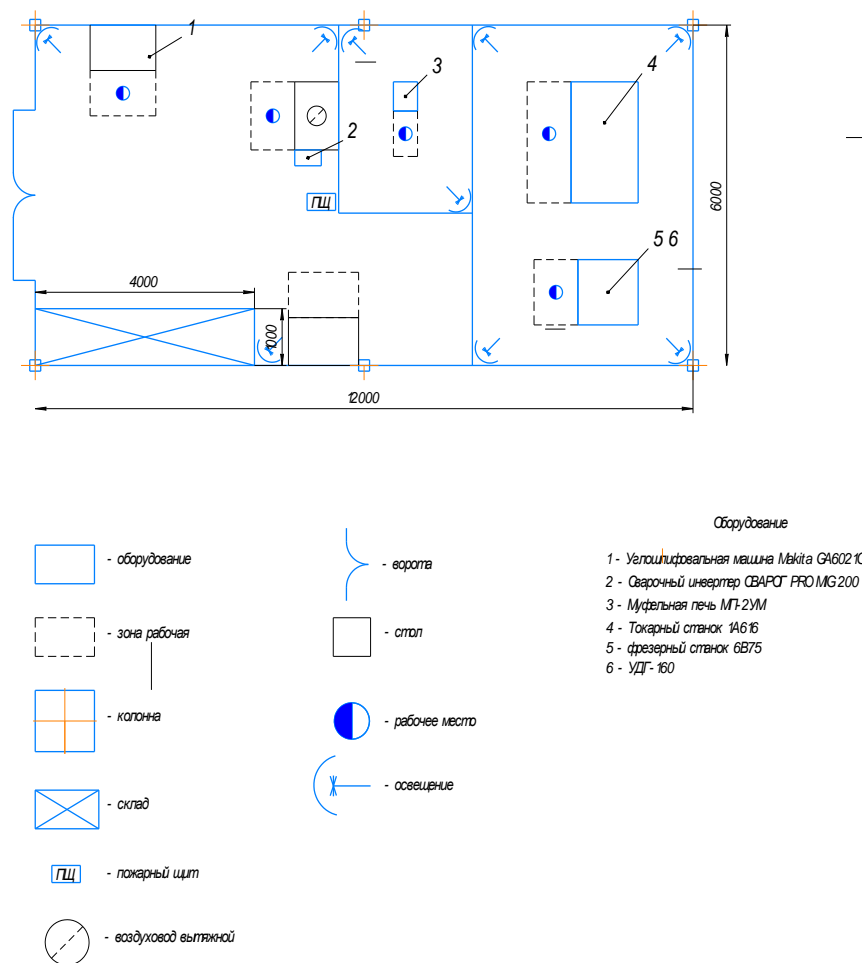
Планировка участка восстановления зубчатого колеса
